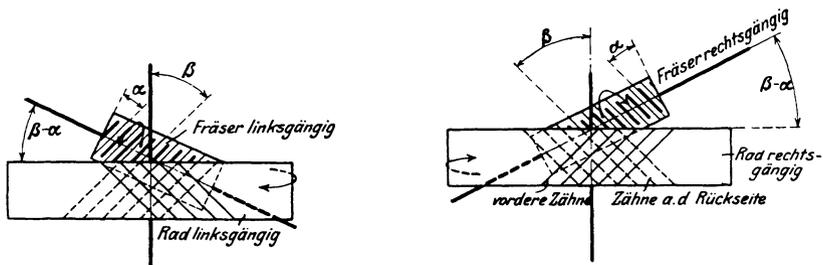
u. 303. Einstellen des Fräasers bei Schraubenrädern.
